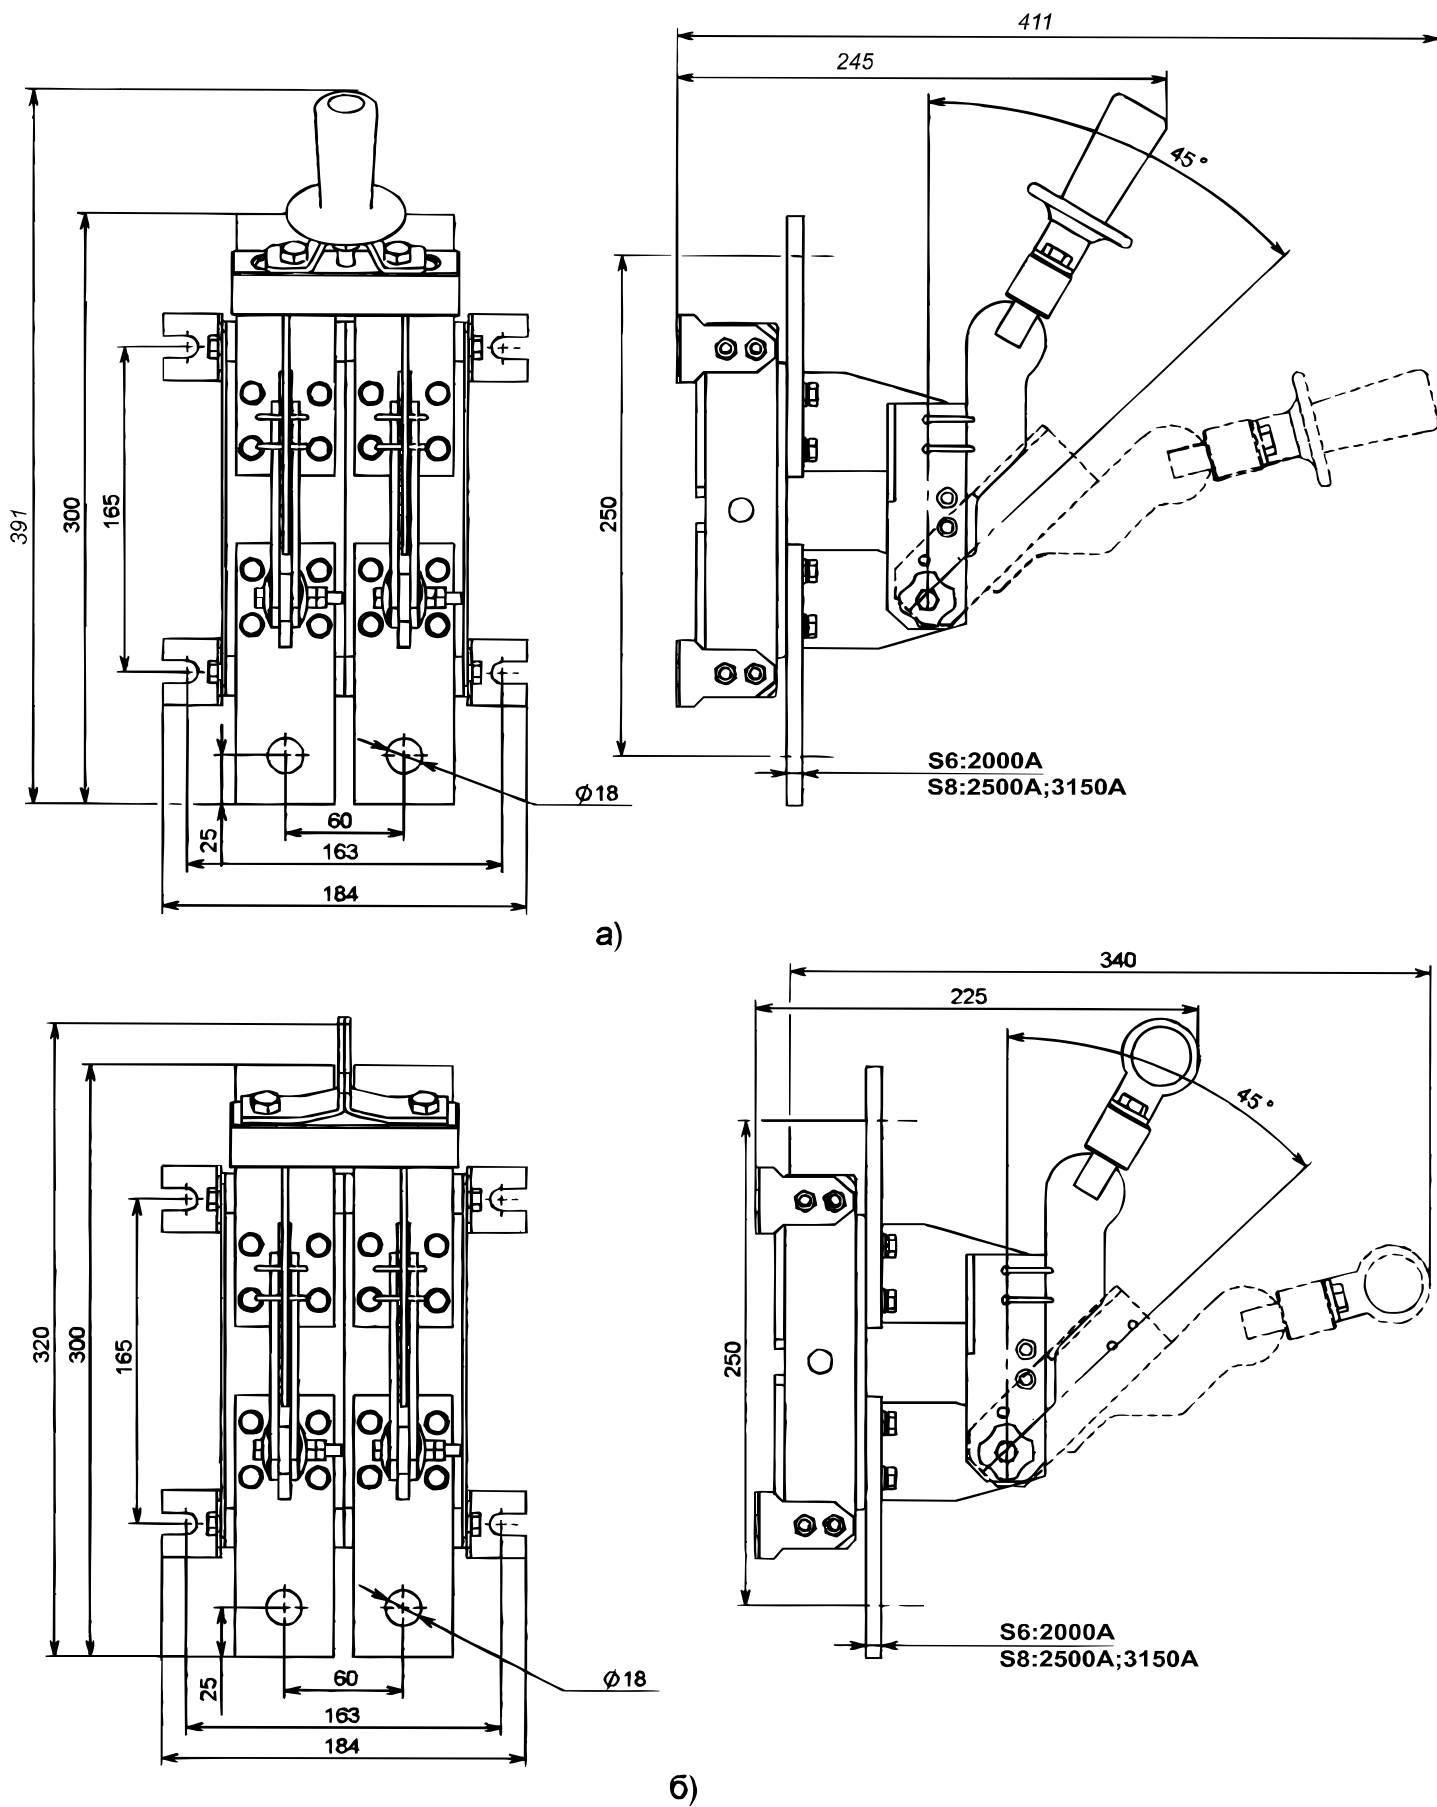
Разъединитель PE19 однополюсный, переднего присоединения шин
